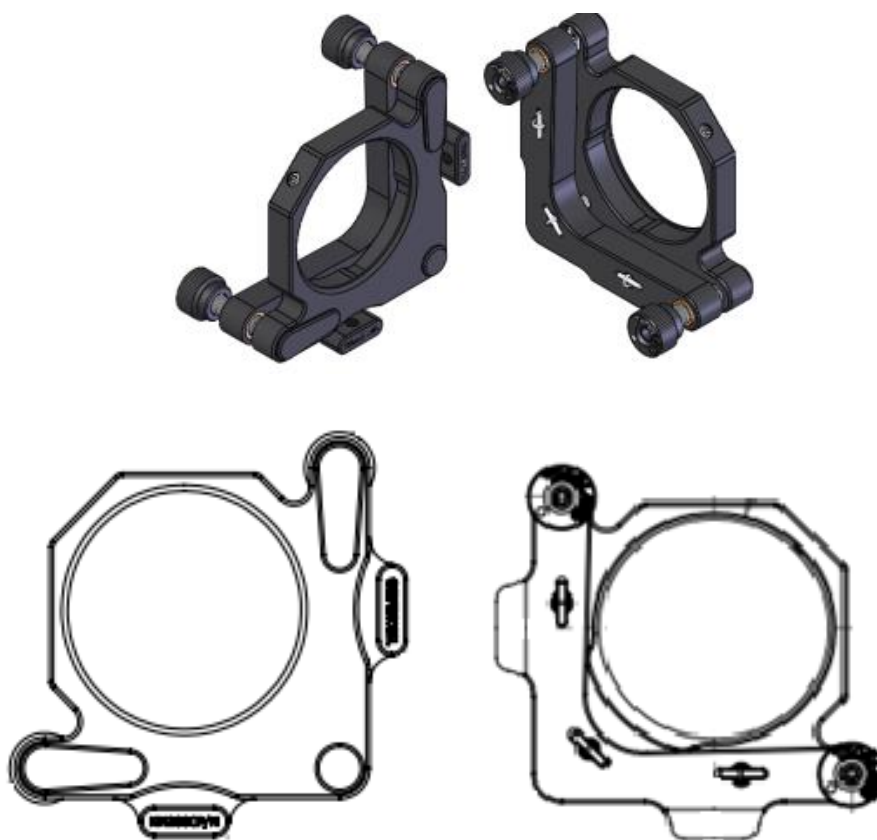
Ескіз механічної частини пристрою для юстирування нерухомого дзеркала
